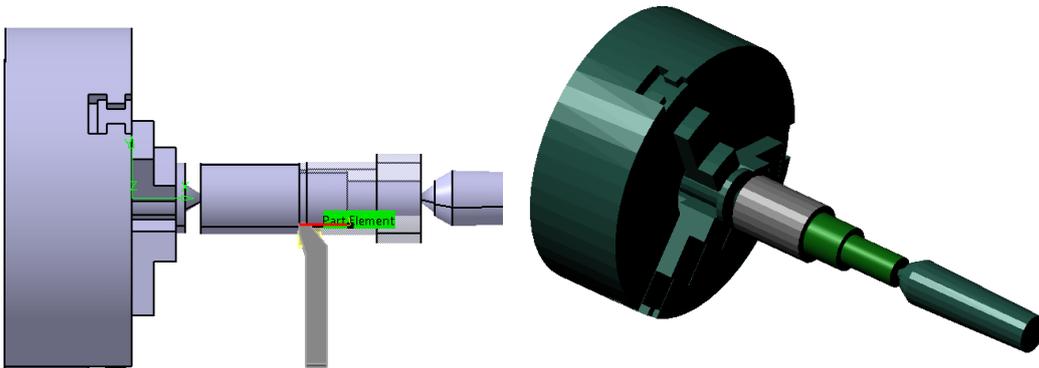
Trayectoria de la herramienta. Figura 6.7 – Geometría tras la operación.
